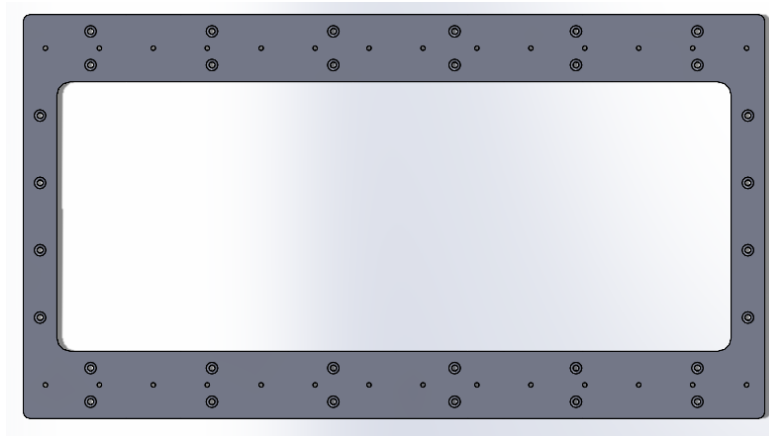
01 Placa soporte en Solidworks. Fuente: propia
